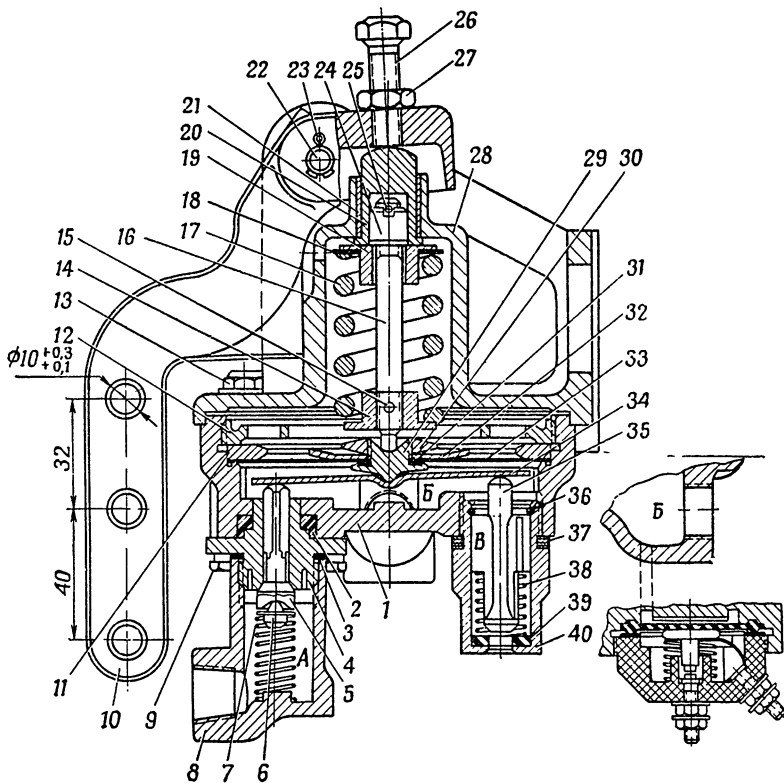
Конструктивная схема одинарного тормозного крана с металлическими диафрагмой и клапанами
